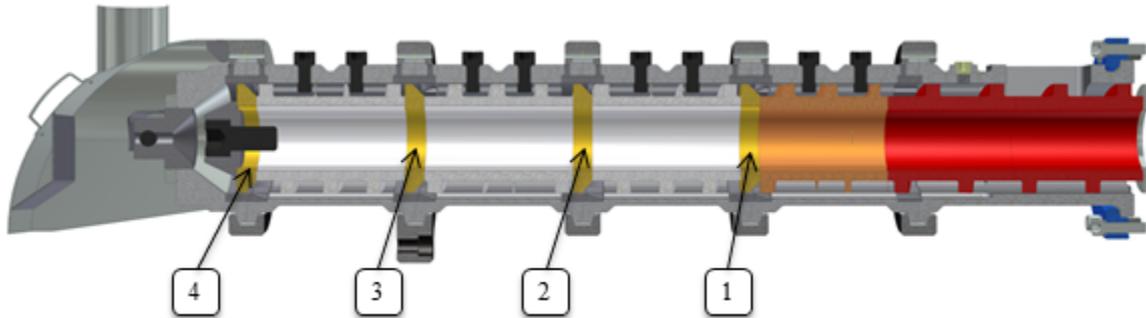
Grundlegende Bestückung mit Drosseleinsätzen (beim Einlaufen des Extruders)
